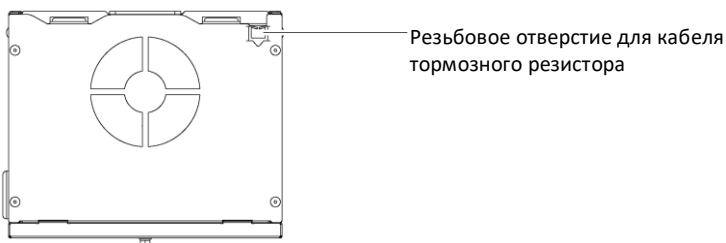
Резьбовое отверстие в верхней части металлического корпуса шкафа управления MR для прохода кабеля тормозного резистора
